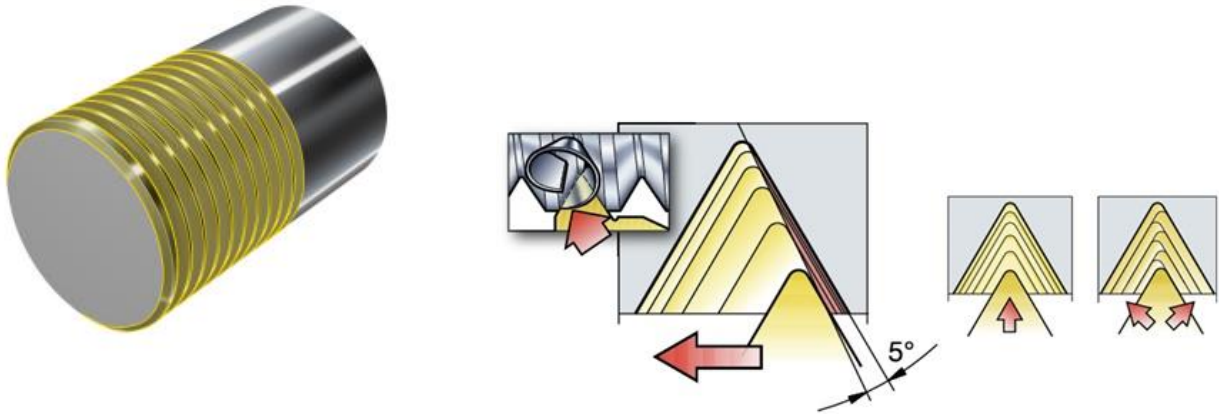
Схема маршруту обробки для поверхні 4 у програмі Sandvik Tool Guide
